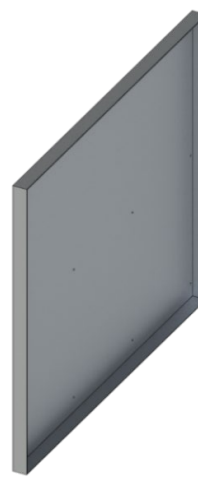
Aislamiento y aluminio de tablero lateral derecho.
